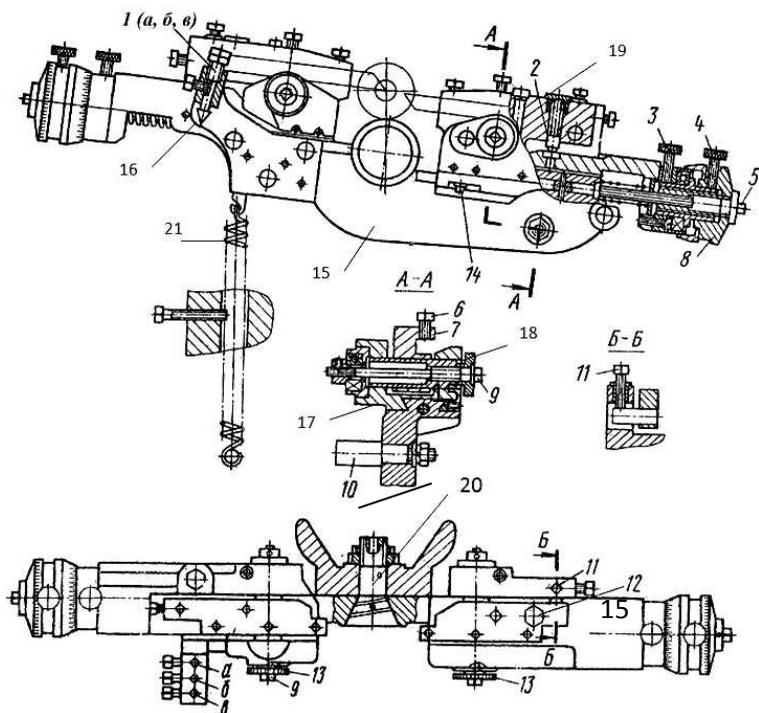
Балансир с суппортами токарного автомата продольного точения
